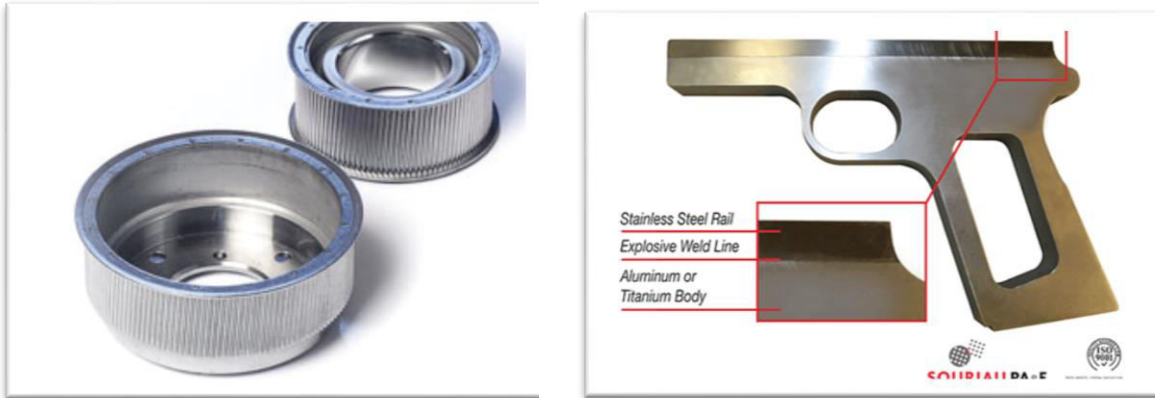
Exemple d'utilisation du procédé de soudage à l'explosif
